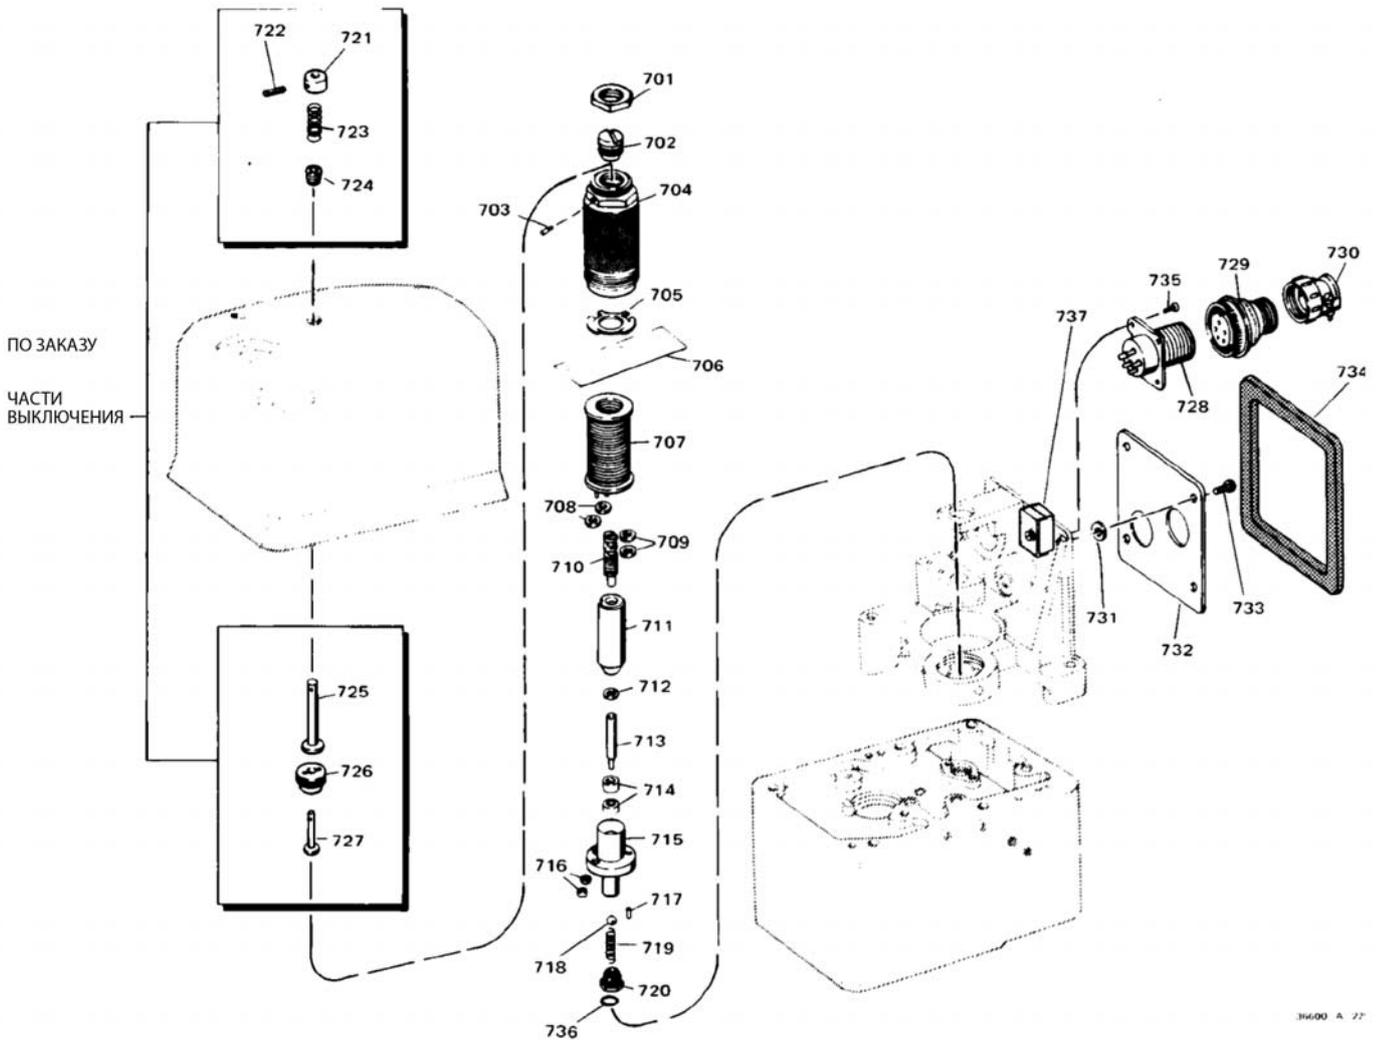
Покомпонентный чертеж, соленоид-выключатель
